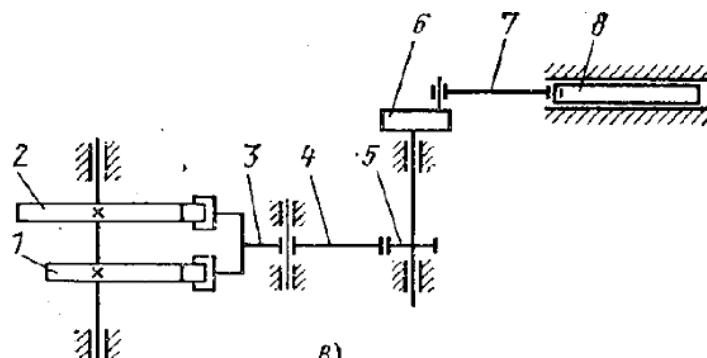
Схема механізму перенесення заготовок багатопозиційних автоматів:
